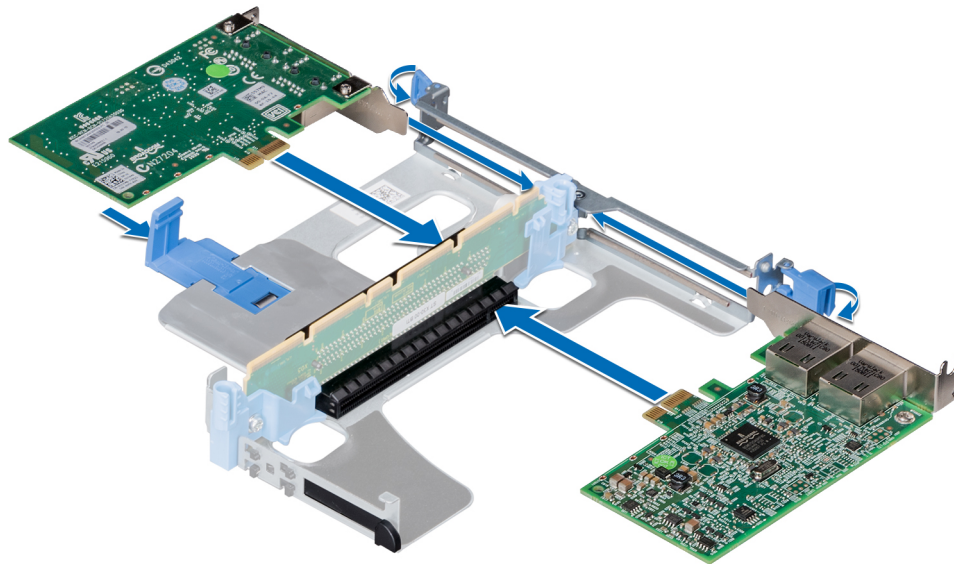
Installation de cartes d'extension dans la carte de montage 1A pour carte d'extension
